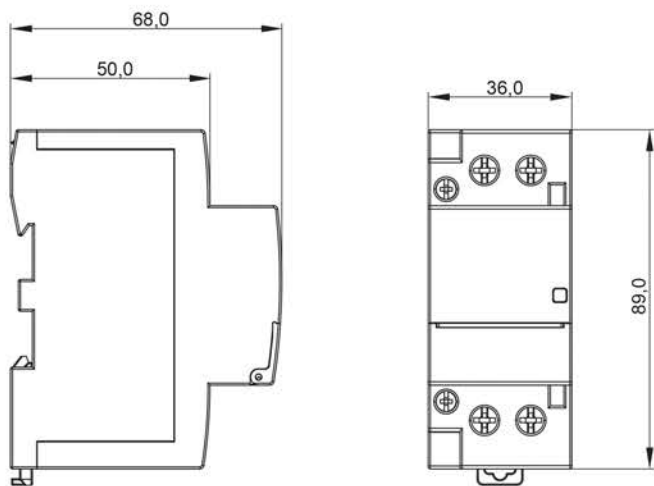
Габаритные размеры контакторов от 40 А до 63 А, 2P / Figure 3 – Overall dimensions of contactors from 40 A to 63 A, 2P
